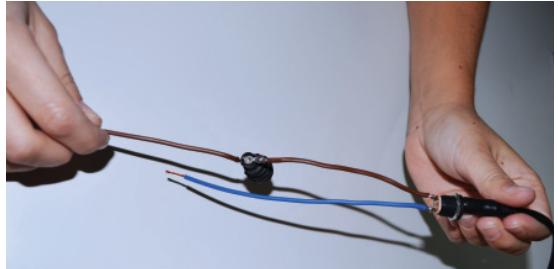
| Portafusible soldado al cable marrón del jack hembra.
